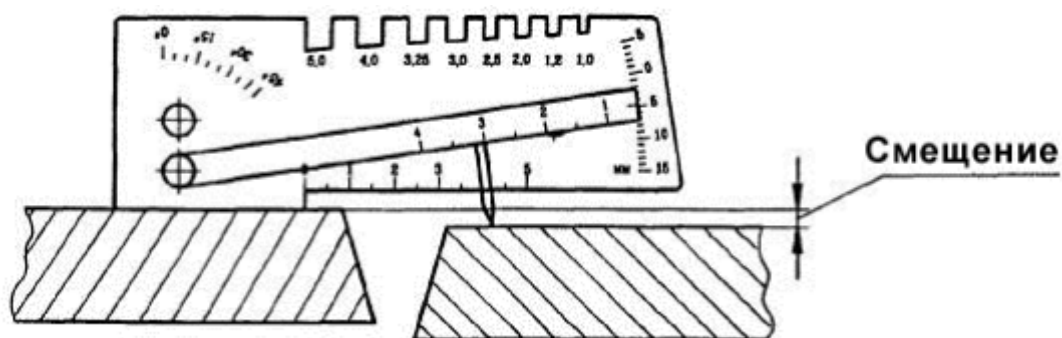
Схема измерения смещений при сварке швов
